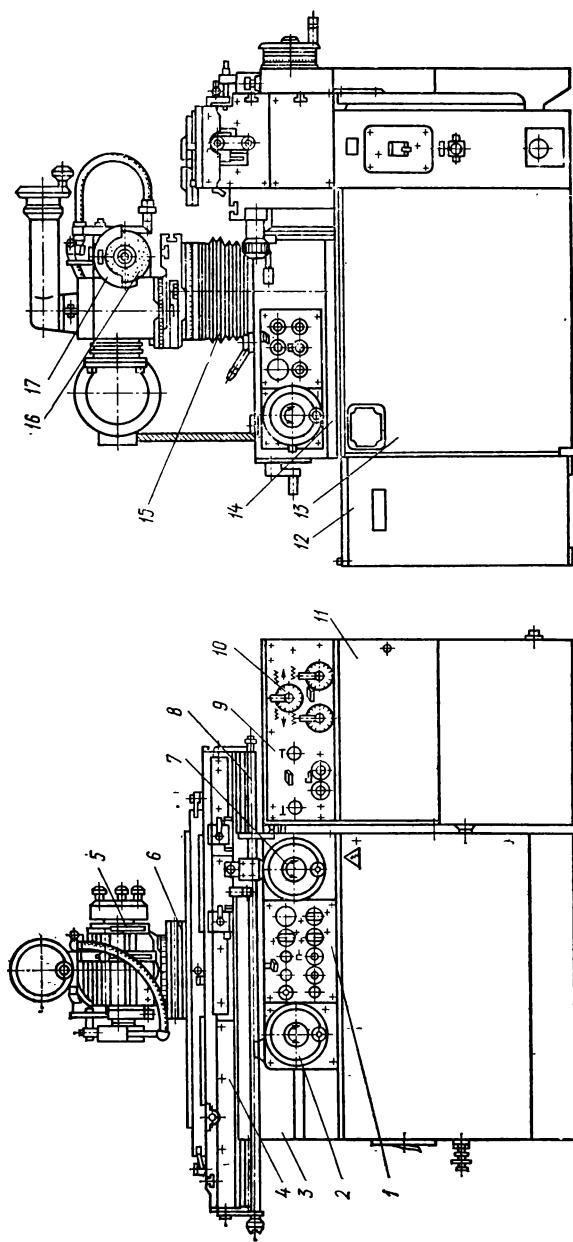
Расположение органов управления универсально-заточного станка мод. 3М642Е:
